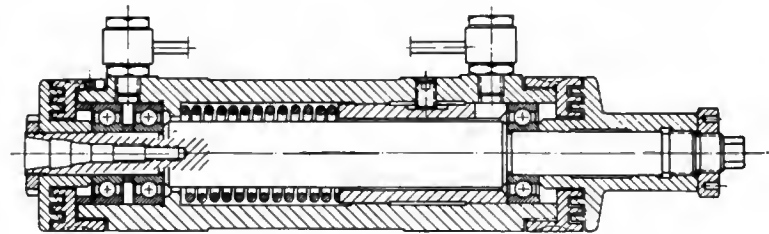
Broche de machine à rectifier pour intérieurs;
